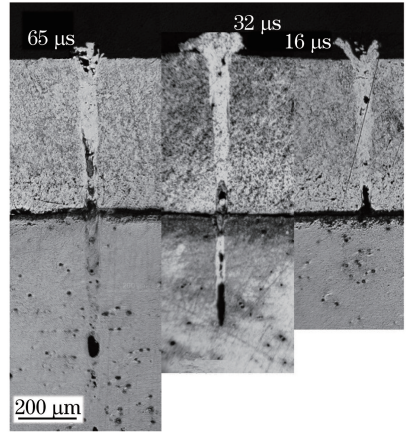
不同激光持续作用时间下的焊缝截面形貌
